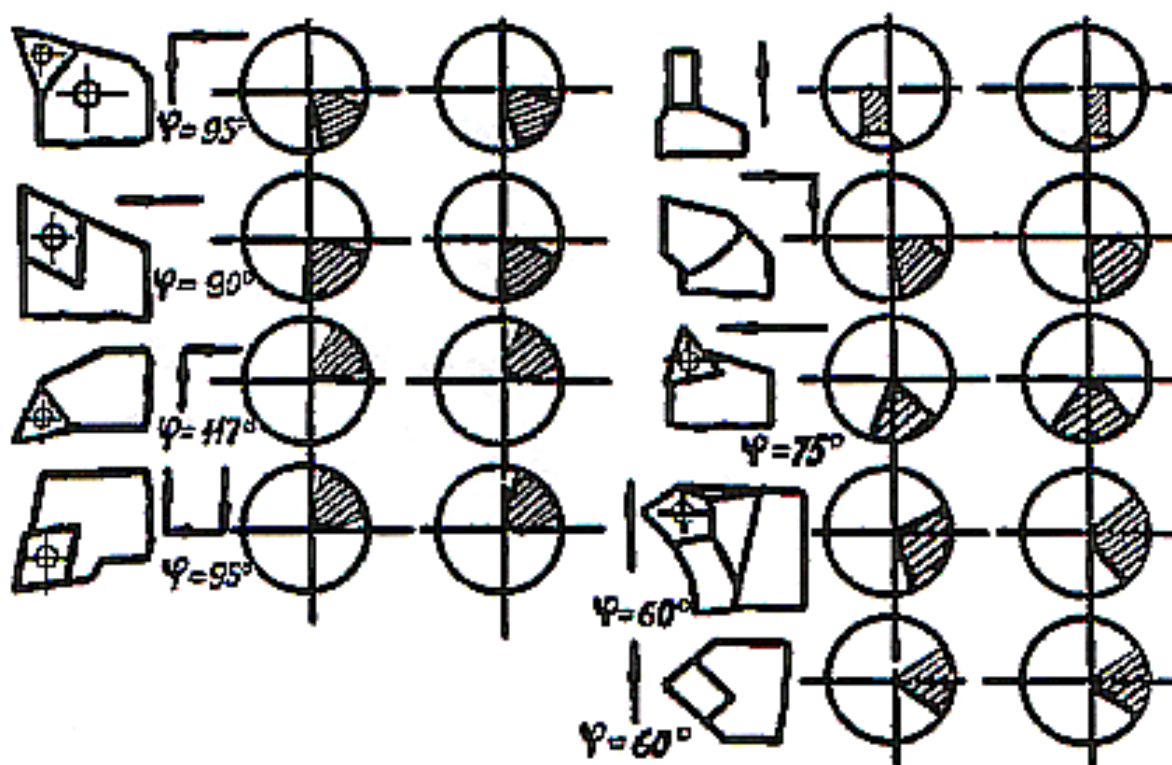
Вид режущих кромок резцов на экране проектора
